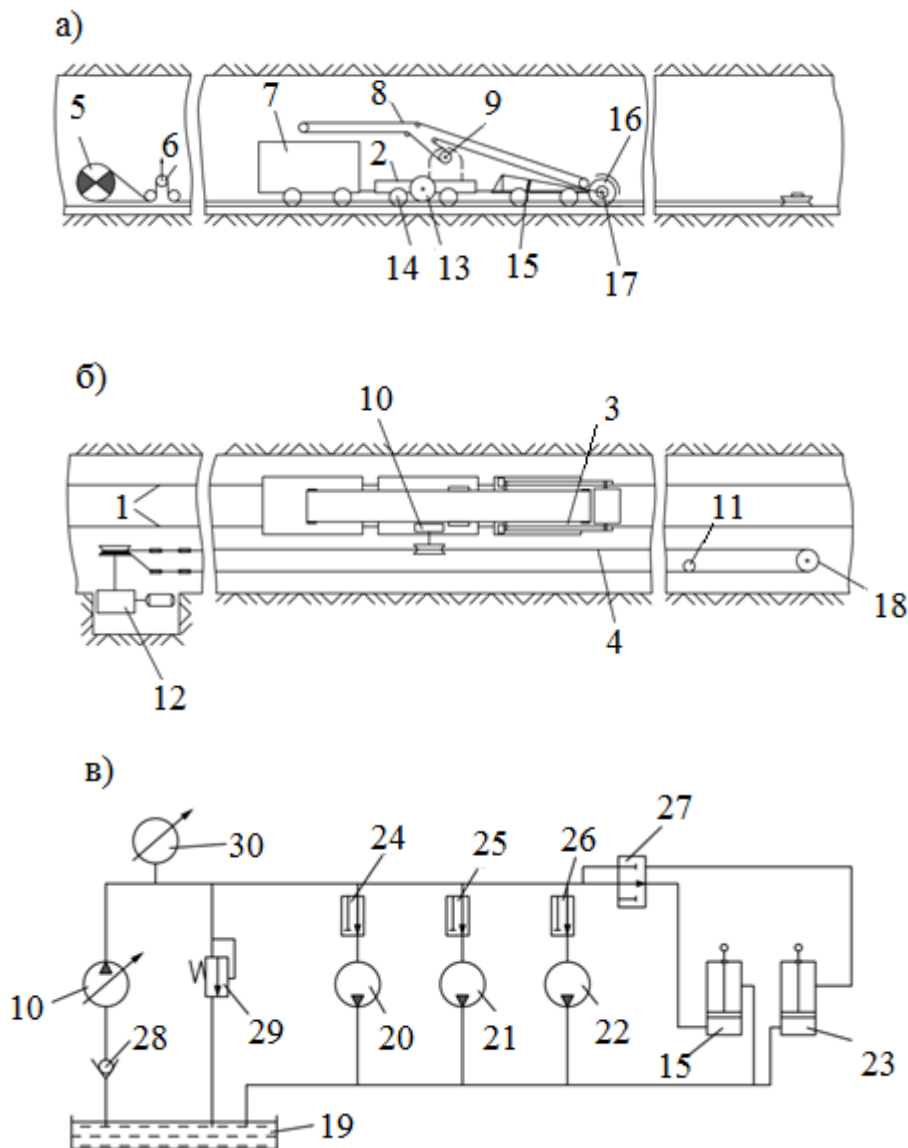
Машина для чистки колій: а – загальний вид збоку; б – вид зверху; в – гідравлічна схема
